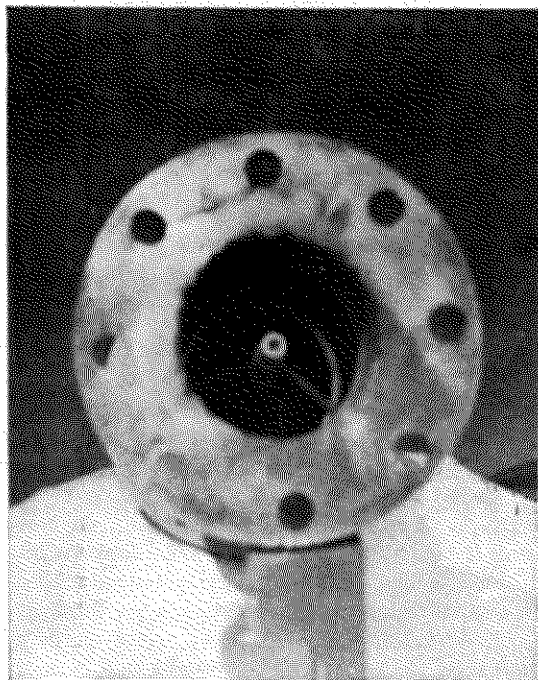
Vista superior da válvula demonstrada na foto anterior.
